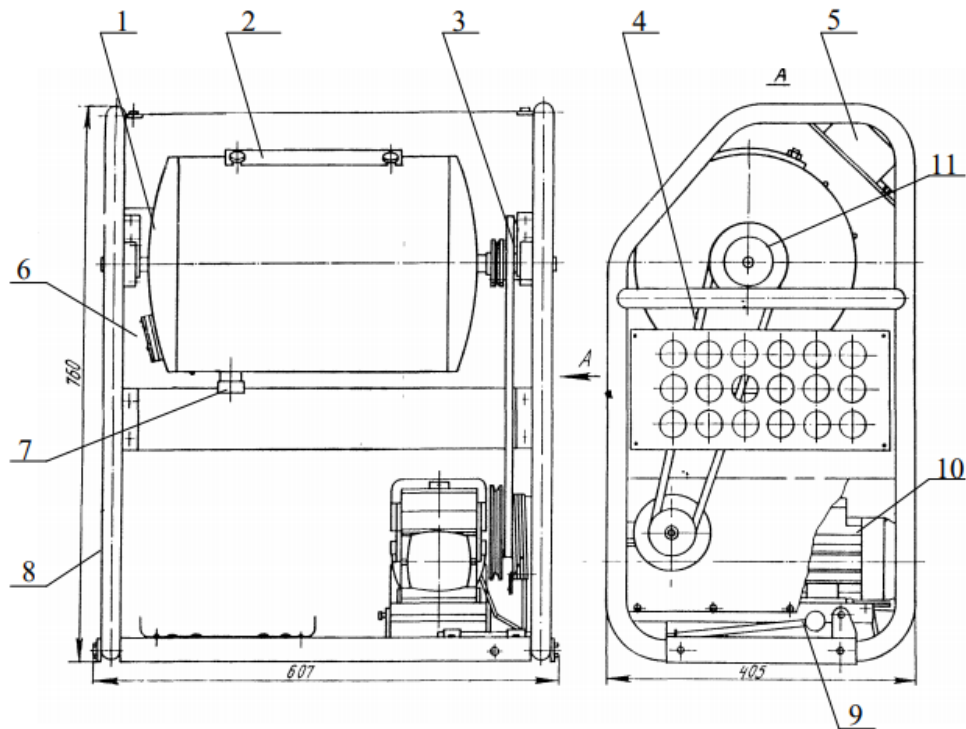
Загальний вид масловичовальника МІП –1500. 1 – ємність; 2 – кришка люка; 3 – підшипниковий вузол; 4 – ремінь; 5 – вимикач електричний; 6 – оглядового вікно; 7 – зливний штуцер; 8 – рама; 9 – ручка підйомника платформи; 10 – привод; 11 – шків.
